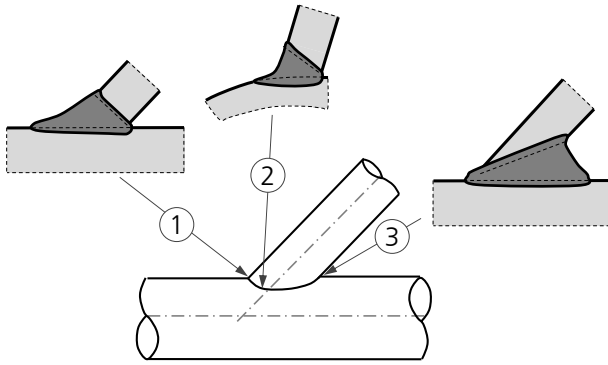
Schweißnahtform entlang der Verschneidung; Ausführung als HV-Naht
